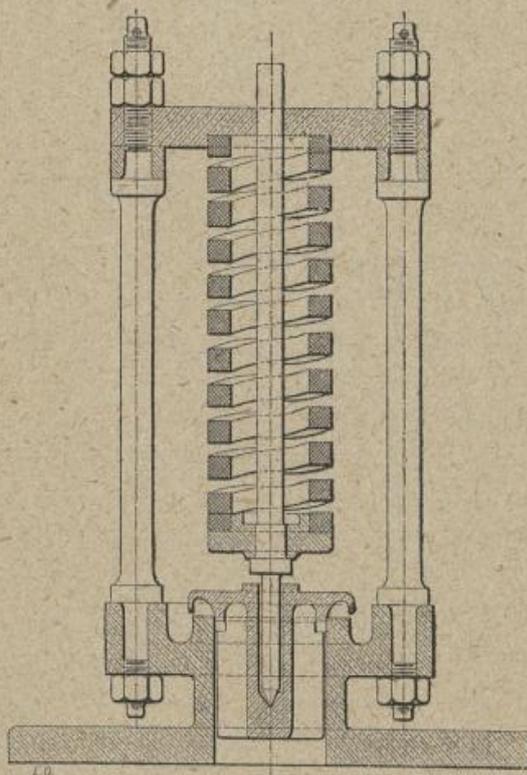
Soupape Adams à gorge et à charge directe, pour locomotives.
